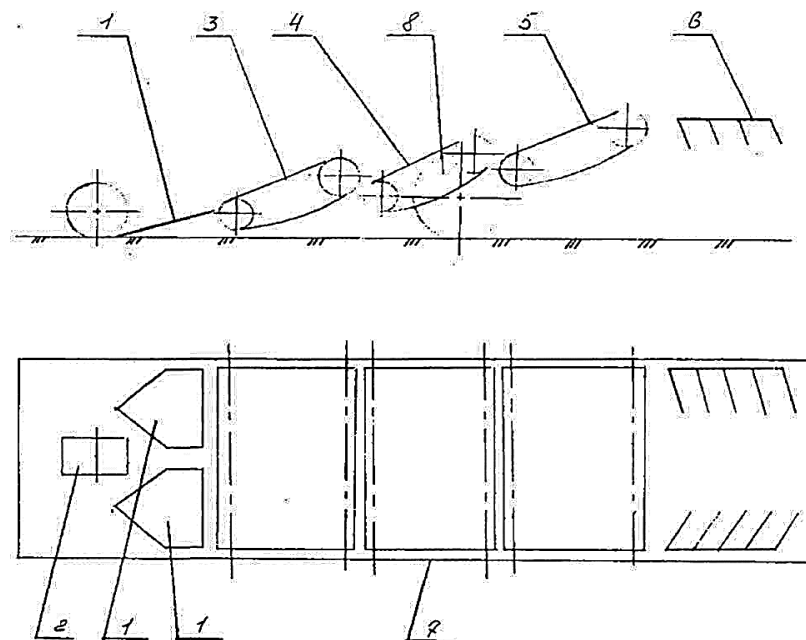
Конструкційна схема копача КСТ-1,4:1 – активні леміші; 2 – копіювальне колесо; 3 – швидкісний елеватор; 4 – основний елеватор; 5 – каскадний елеватор; 6 – щитки для утворення валка; 7 – рама; 8 – ходове колесо.
